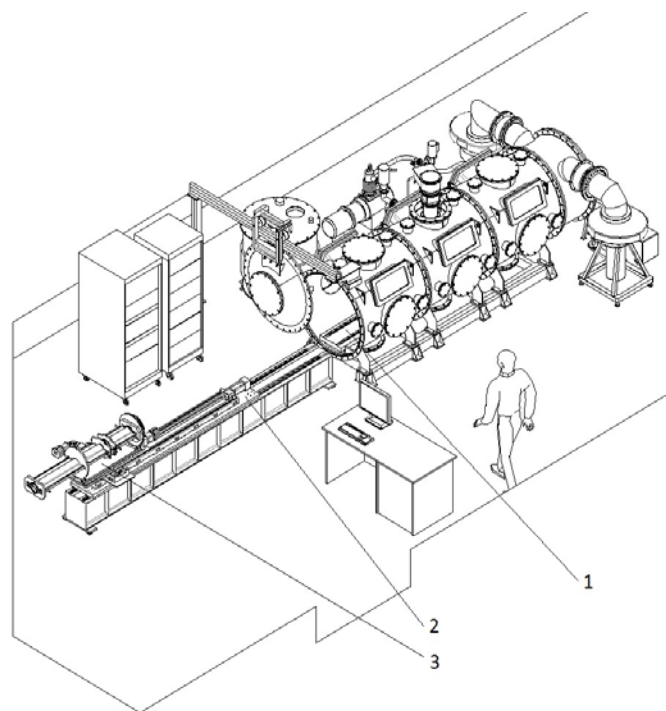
Схема установки электроннолучевой сварки. 1 – нижняя неподвижная платформа; 2 – верхняя подвижная платформа; 3 – механизм вращения свариваемой детали вокруг его продольной оси и модули линейного перемещения.
